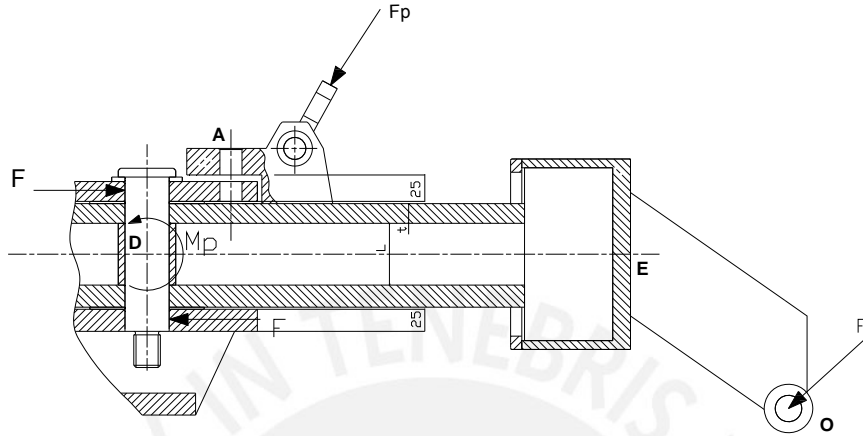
SECCIÓN DE BARRA DE GIRO HORIZONTAL.
